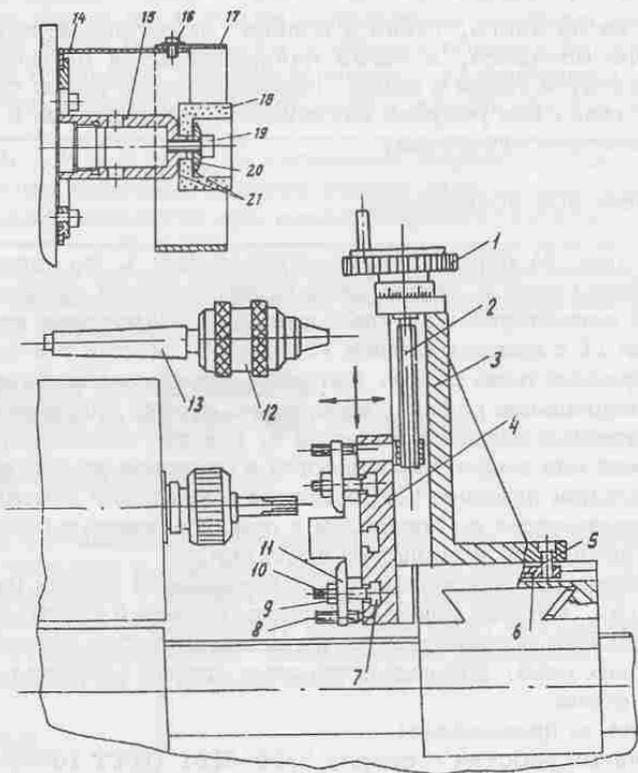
Фрезерно-сверлильное и плоскошлифовальное устройство.
